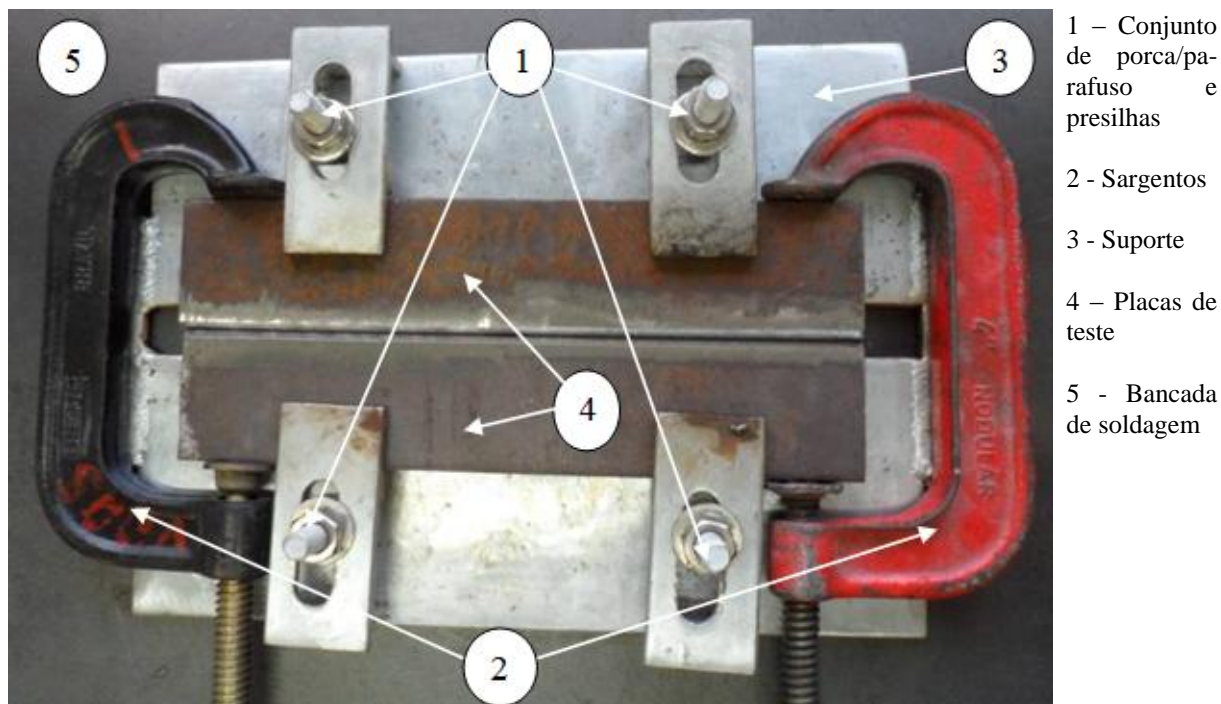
Vista superior do suporte utilizado para fixar as placas de teste e possibilitar a soldagem
